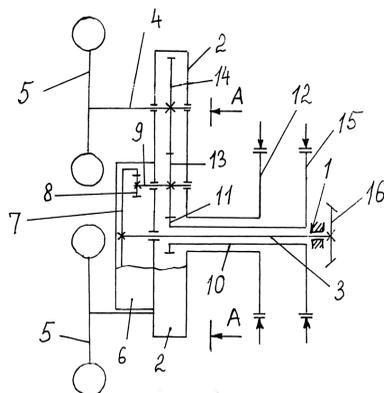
Кинематическая схема движителя (вид сбоку)
